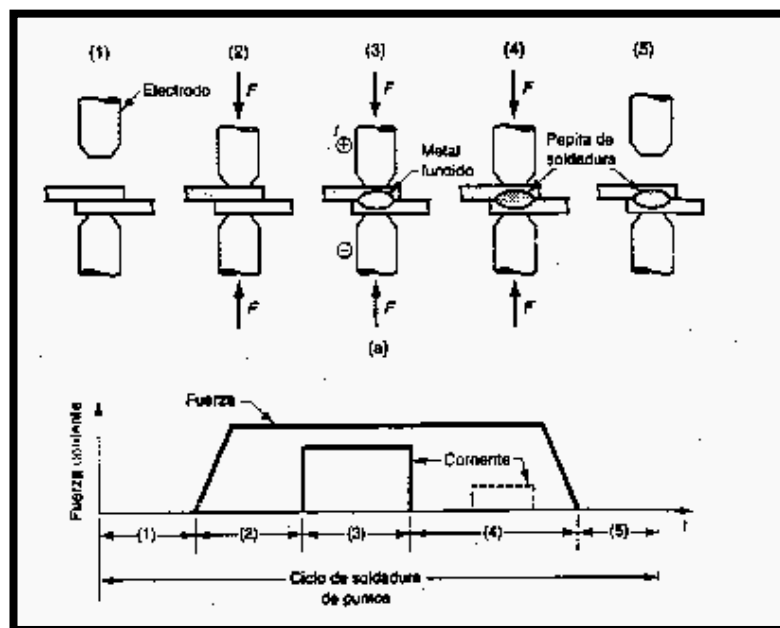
PASOS DEL CICLO DE SOLDADURA DE PUNTO
